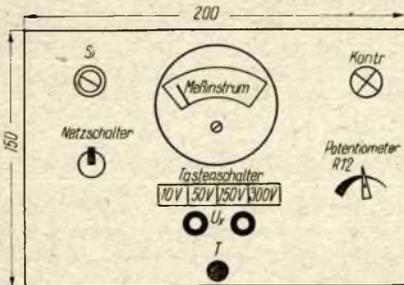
Aufbauvorschlag für die Frontplatte des beschriebenen Röhrenvoltmeters
